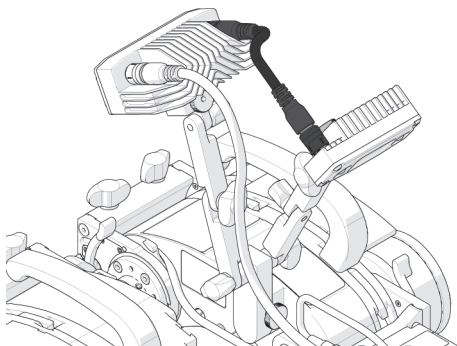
Collegamento del cavo della fotocamera secondaria a entrambe le fotocamere
